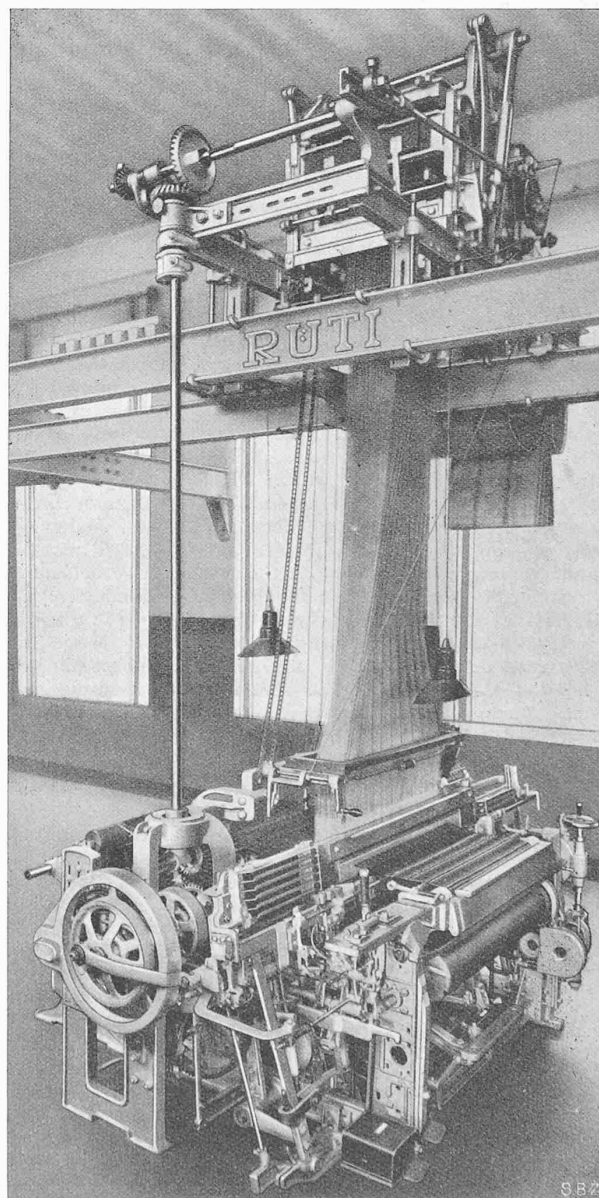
Sechsschütziger Seidenlancierstuhl mit Jacquardmaschine
